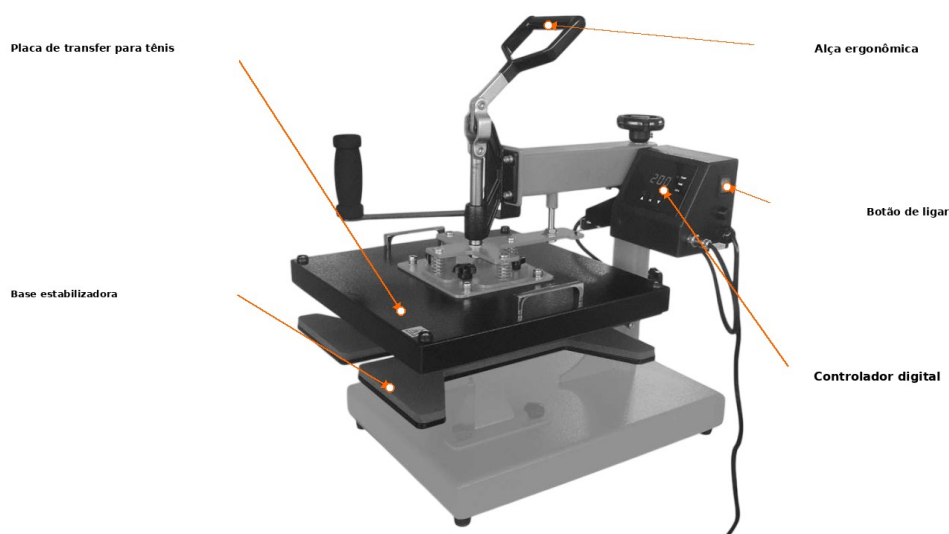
· Componentes principais do equipamento Beinsen Chinela.
